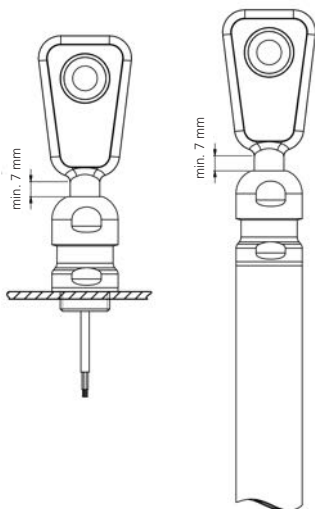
pms-Sensor D12-Adapterschaft mit Sensorverschraubung BF-pms/A1 befestigt am Maschinenteil oder am Edelstahlrohr D26,8 mit Innengewinde M20x1,5
